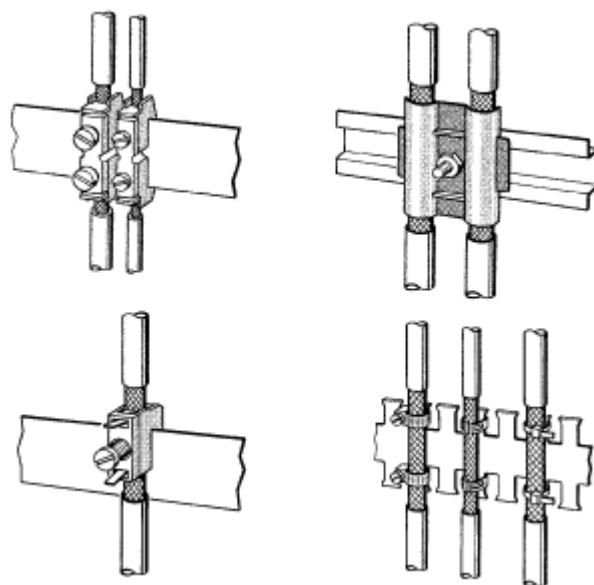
Fissaggio dei cavi schermati con fascette serracavi ed elemento di collegamento per tubi (rappresentazione schematica)
